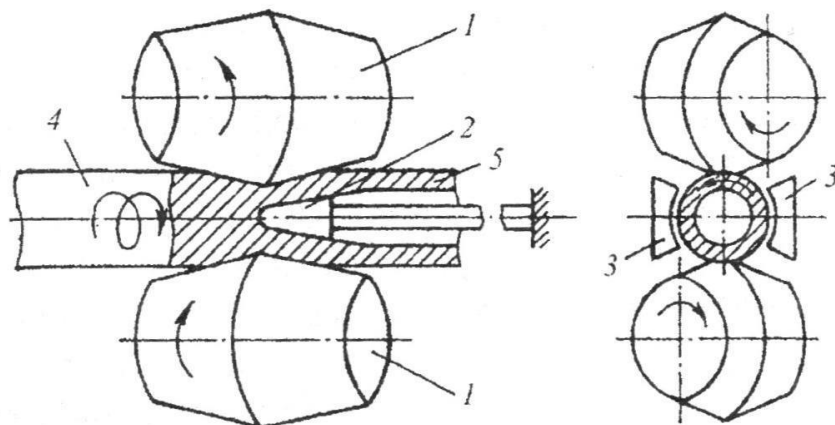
Схема поперечно-гвинтового прокатування на прошивному стані для отримання отвору у суцільній заготовці: 1 – прокатні валки; 2 – оправка; 3 – утримуючі лінійки; 4 – трубна заготовка, 5 – готова труба
